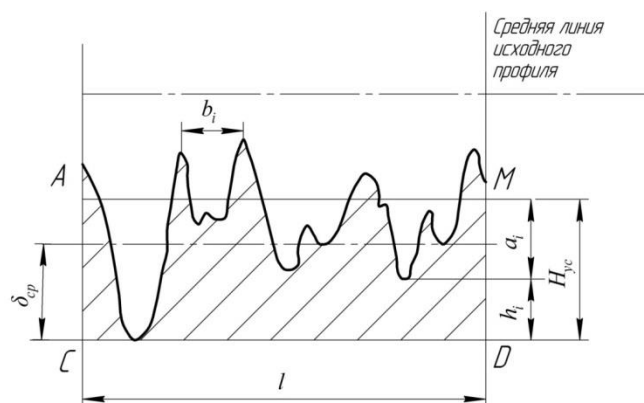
Схема образования профиля шероховатости поверхности при обработке свободными абразивами
